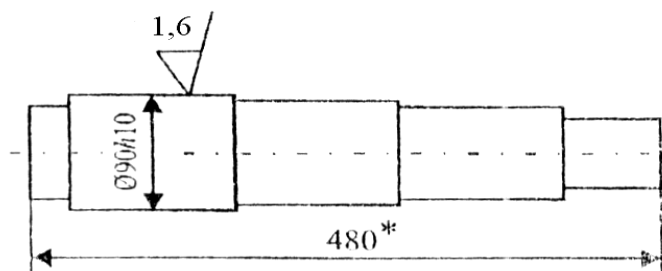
Схема полів допусків зовнішньої поверхні деталі за умов механічної обробки
